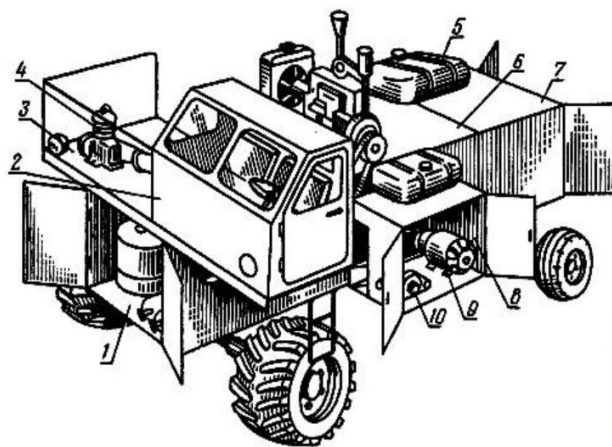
Схема комбинированного передвижного агрегата для ремонта и обслуживания тракторов, зерноуборочных комбайнов и другой сельскохозяйственной техники: 1 – место для размещения газосварочной аппаратуры; 2 – кабина; 3 – прямоугольная площадка; 4 – компрессор; 5 – бак для масла; 6 – металлическая емкость для воды; 7 – отсек для инструмента; 8 – отсек для сварочного генератора; 9 – генератор; 10 – водяной насос
